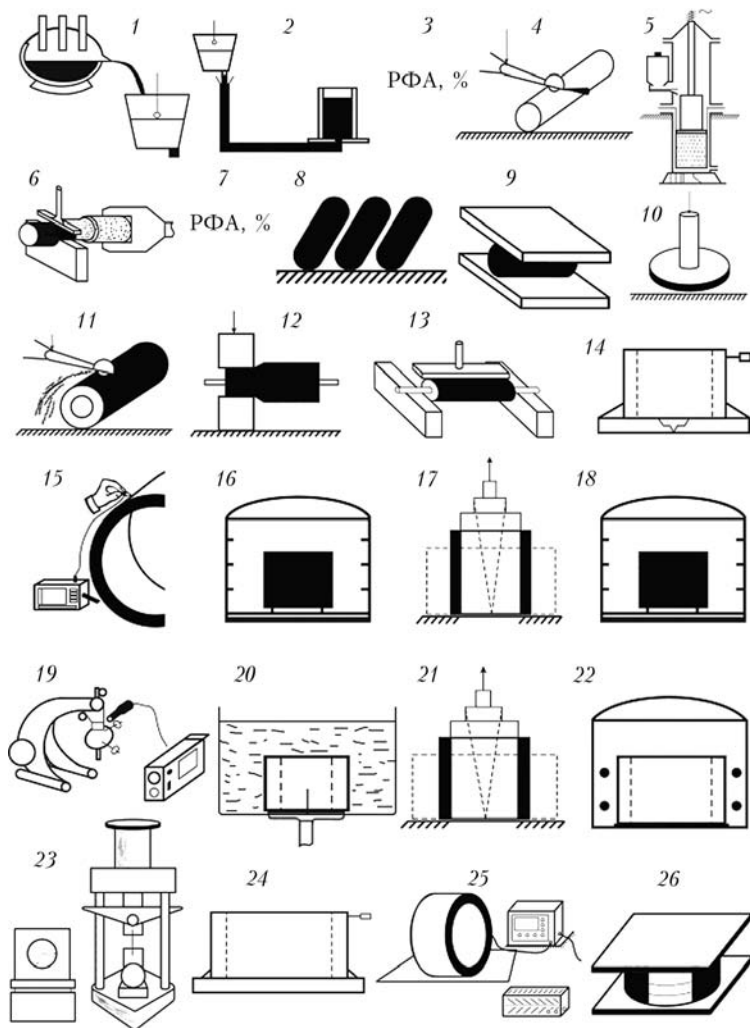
Технологическая схема приготовления бандажного кольца, включающая следующие операции: 1 – выплавку; 2 – разливку металла; 3 – рентгенофлуоресцентный анализ (РФА); 4 – обтачивание; 5 – электрошлаковый переплав под давлением; 6 – первичную ковку; 7 – РФА; 8 – резку; 9 – высадку; 10 – сверление; 11 – обдирку; 12 – медленную ковку; 13 – раскатку; 14 – грубую обработку; 15 – ультразвуковую дефектоскопию; 16 – термообработку на твердый раствор (ТТР); 17 – закалку; 18 – холодную растяжку (ХР); 19 – ТТР; 20 – контроль структуры; 21 – ХР; 22 – снятие остаточных напряжений; 23 – устройство исследования механических характеристик; 24 – финишную доводку; 25 – неразрушающий контроль; 26 – упаковку
